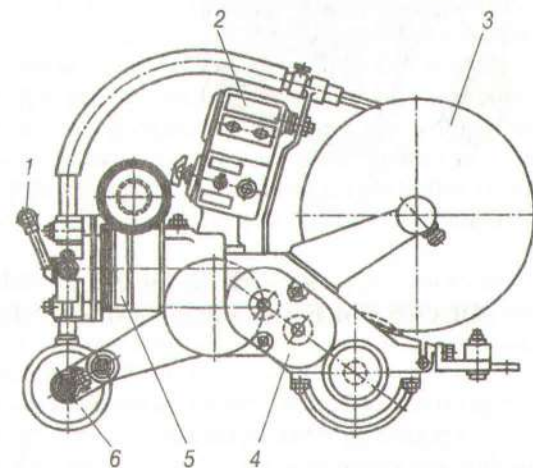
Універсальний зварювальний трактор ТС-42:
